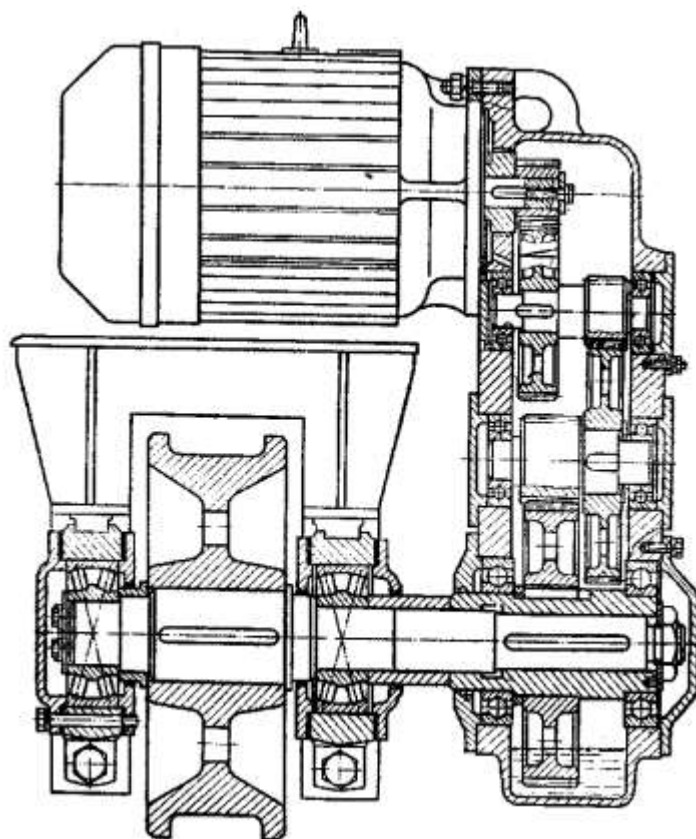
Установка раздельного привода с навесным редуктором и с фланцевым электродвигателем
